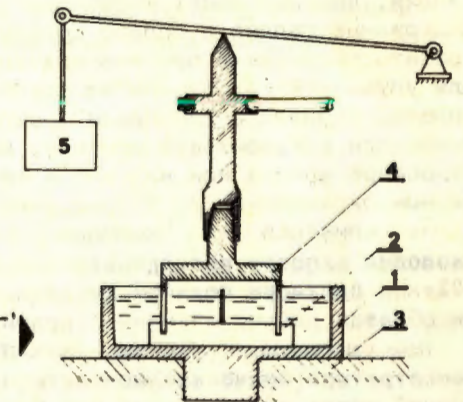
Приспособление для вырезки круглых заготовок из германия.
